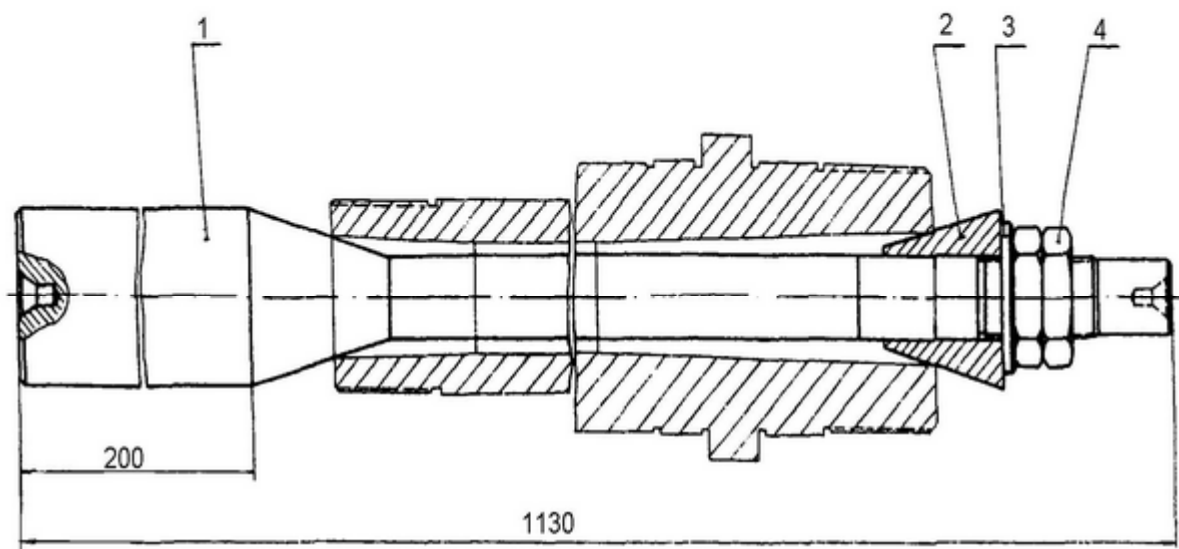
Оправка для обработки шпинделя СД 7111 – 4008
